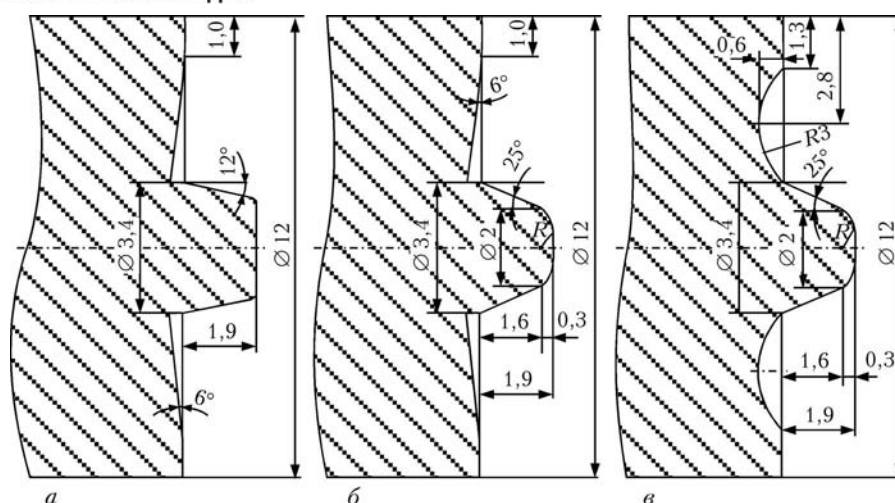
Эскизы рабочих частей инструментов с конической (а, б) и полусферической (в) канавками на рабочей поверхности бурта и различной формой наконечников для СТП алюминиевых сплавов толщиной 2 мм
